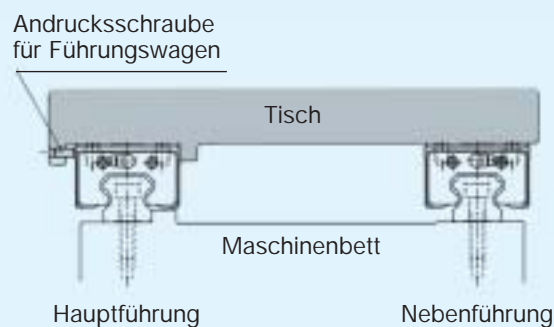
Beispiel für Montage ohne Andruckschrauben für Führungsschienen auf der Hauptführungsseite
